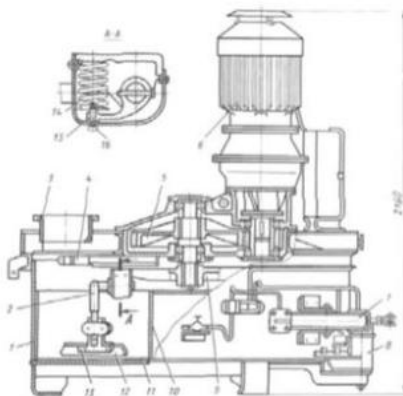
Роторный смеситель вместимостью с верхним расположением привода и цилиндрическим редуктором:
